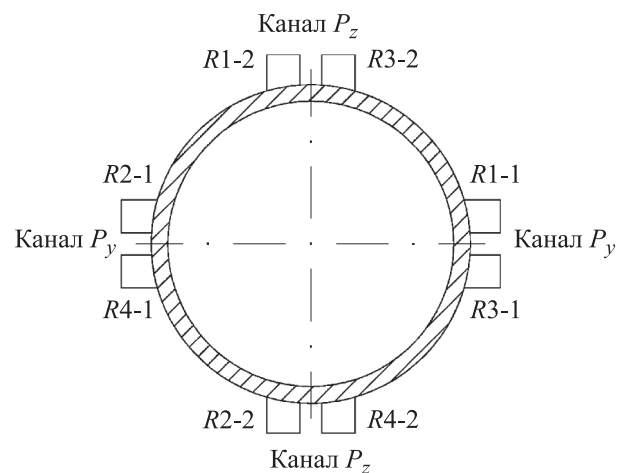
Схема расположения тензорезисторов на корпусе шпинделя
